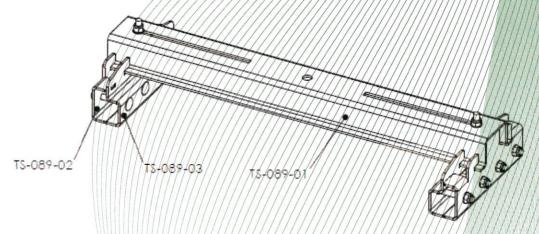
Anschlageinrichtung, Typ: TS STFA/Easy
